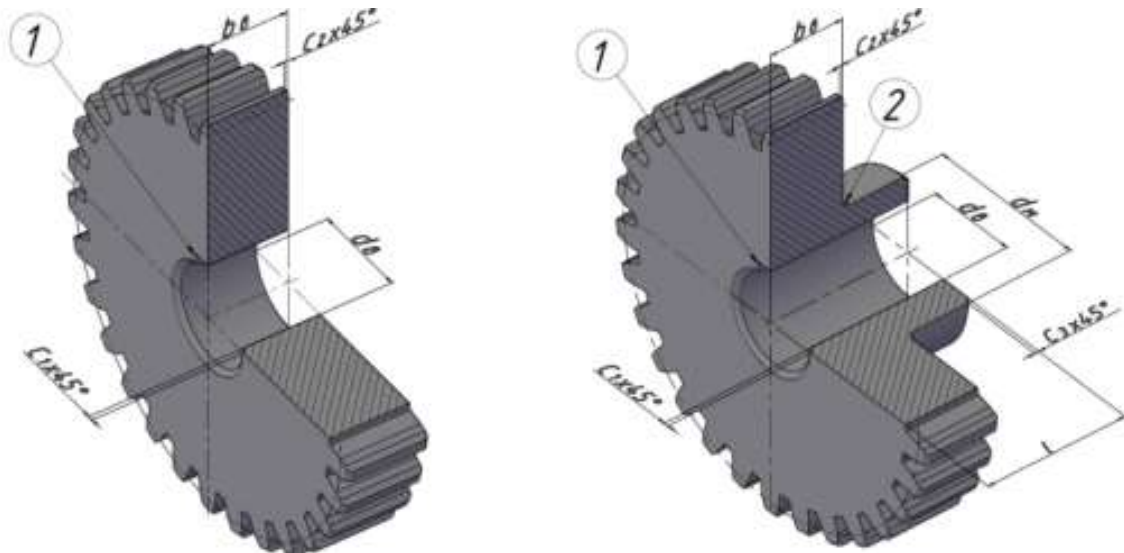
Зображення деталей для виконання робочого кресленника «Колесо зубчасте»
